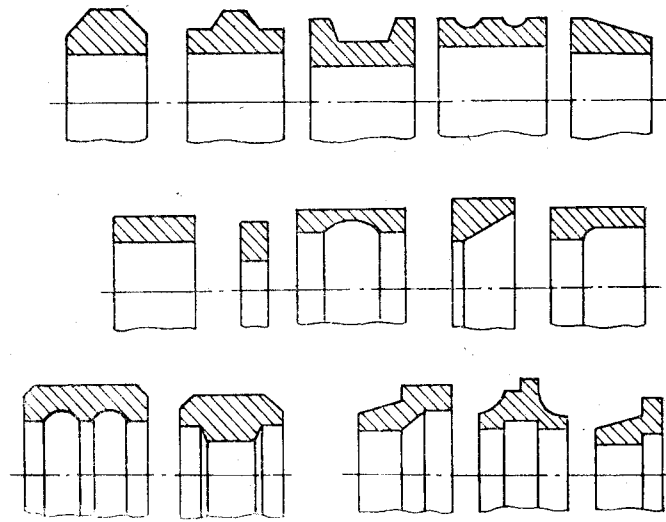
Форми перетинів кільцевих заготовок, виготовлених розкатуванням.
